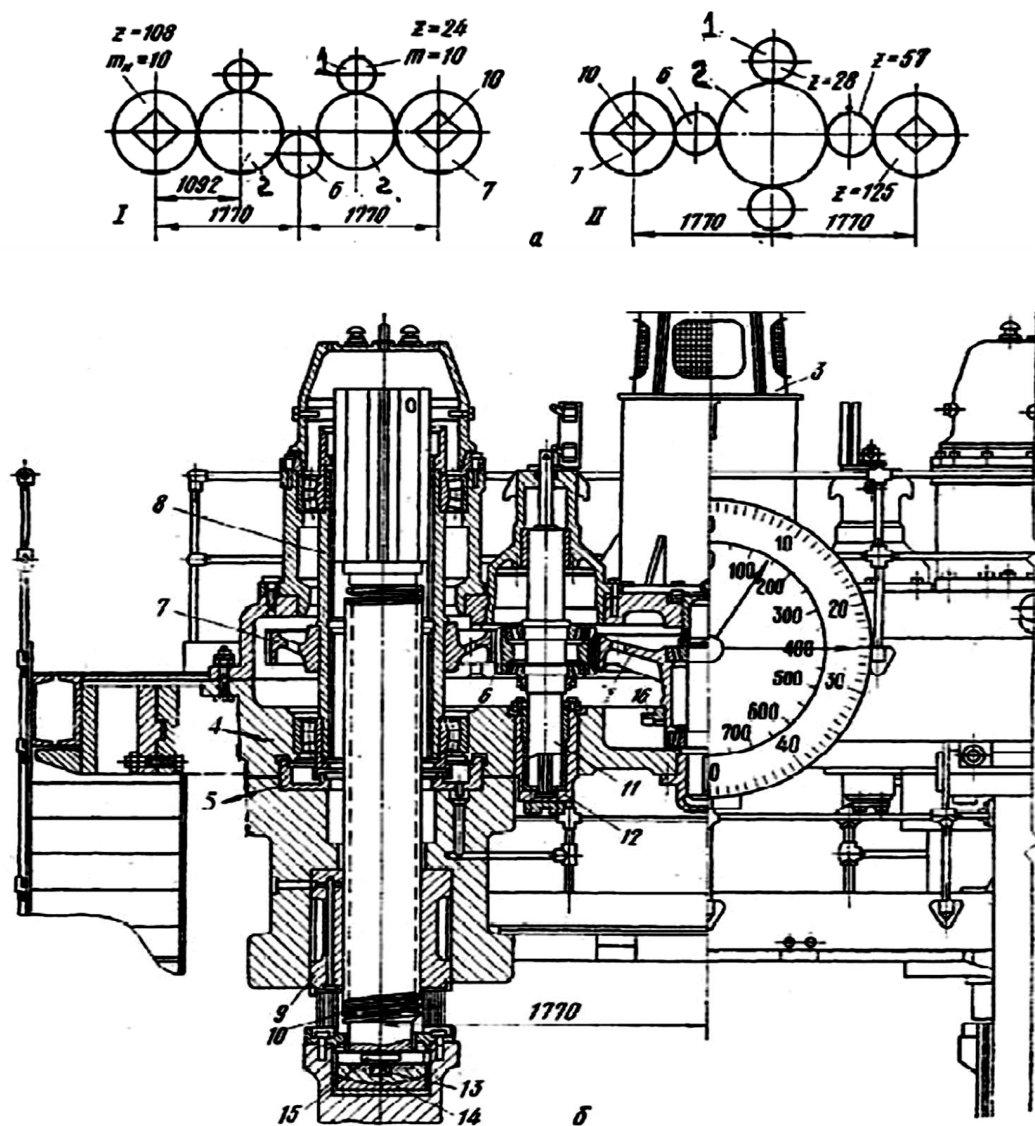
Быстроходные устройства для установки валков блюминга:
